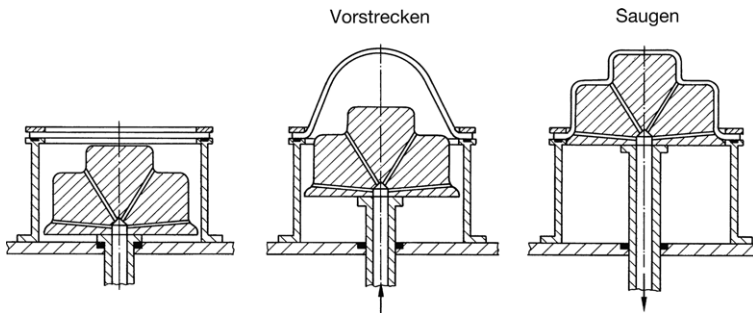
Positiv-Saugen mit Vorstrecken durch Druckluft
